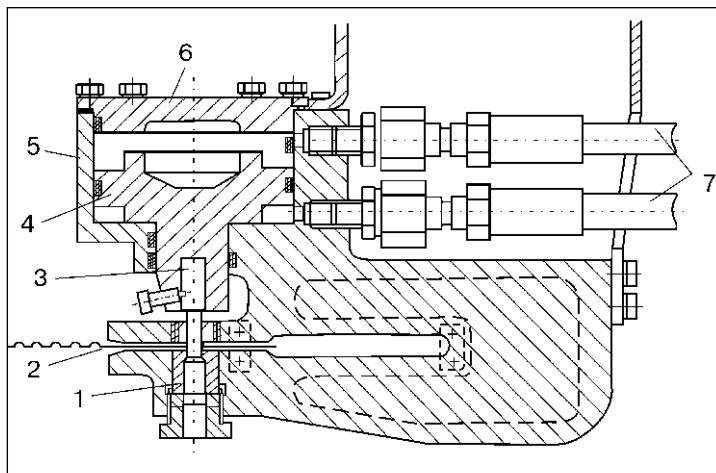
Головка-пресс специализированной установки для пробивки отверстий: 1 — матрица; 2 — лист семизиговой обшивки; 3 — пуансон; 4 — цилиндр; 5 — корпус головки-пресса; 6 — крышка; 7 — шланг высокого давления
